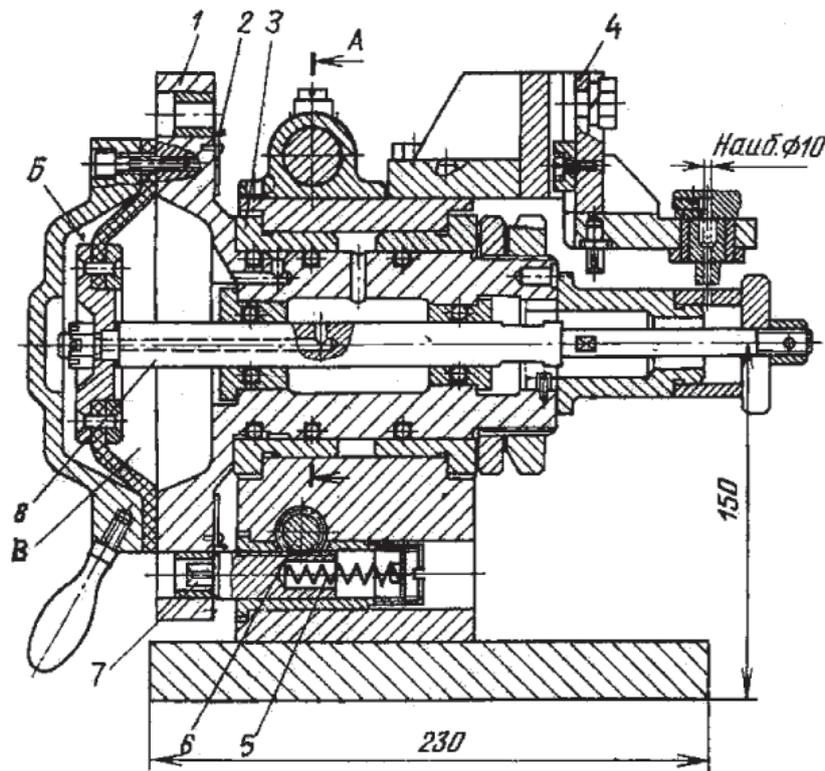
Кондуктор переналаживаемый для групповой обработки радиально расположенных отверстий
